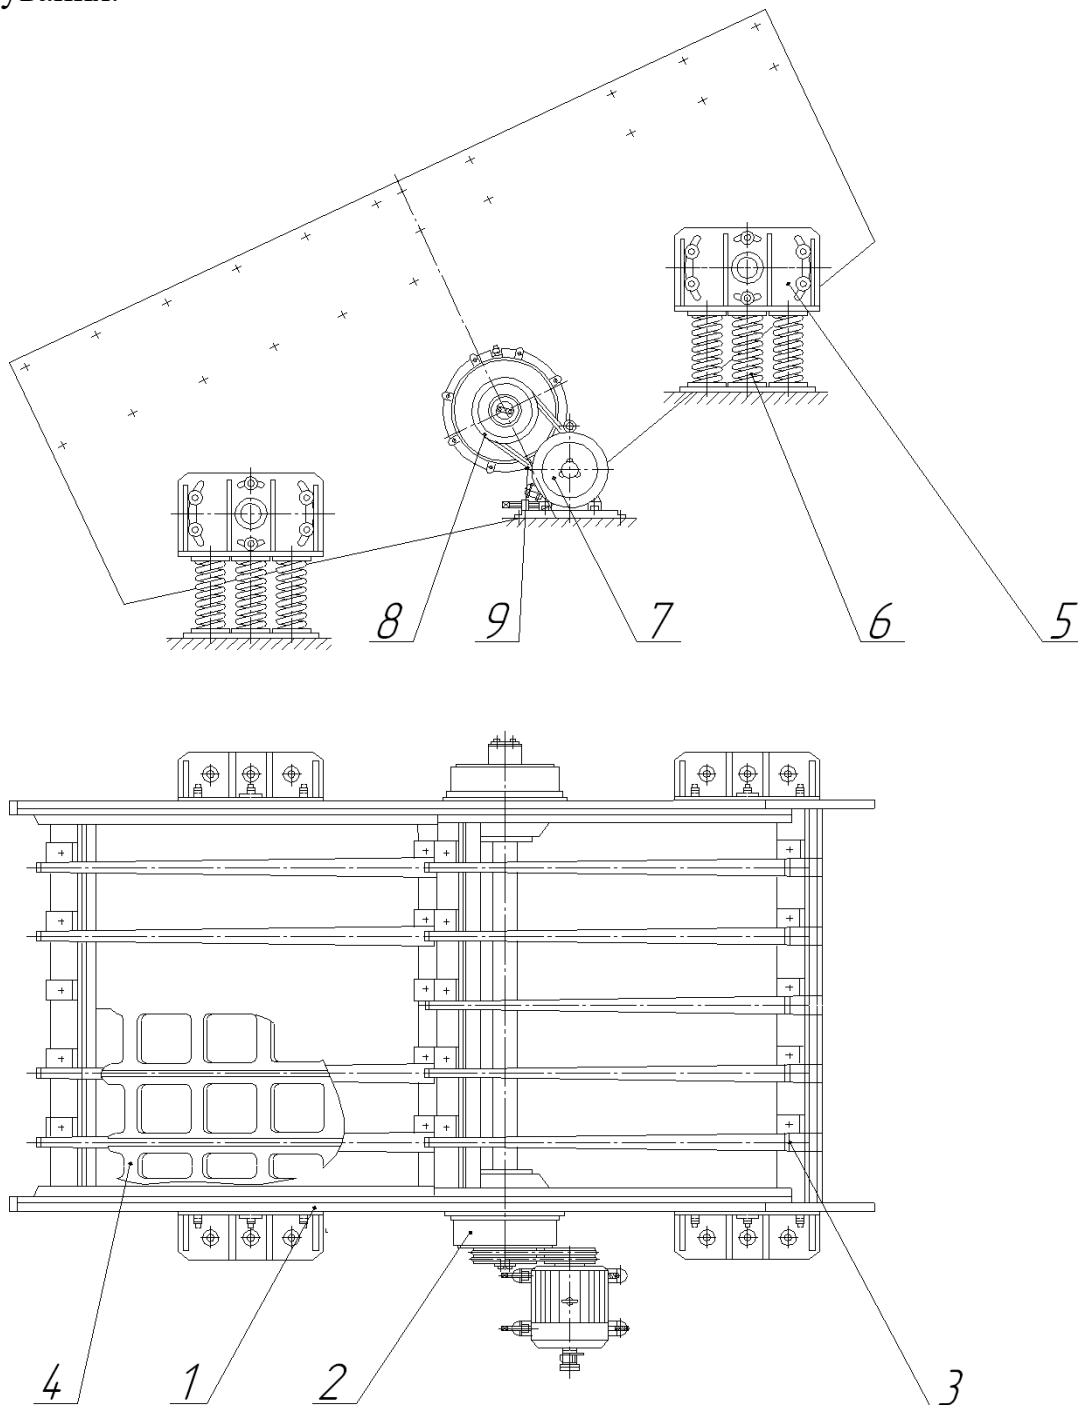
Грохот колосниковий інерційний (1 – футерований короб; 2 – вібратор; 3 – колосник; 4 – ґратки; 5 – кронштейн; 6 – пружина; 7 – електродвигун; 8 – шків ведений; 9 – клинопасова передача)
